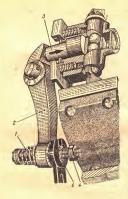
Регулировка привода ручного тормоза автомобиля ГАЗ-51А:
